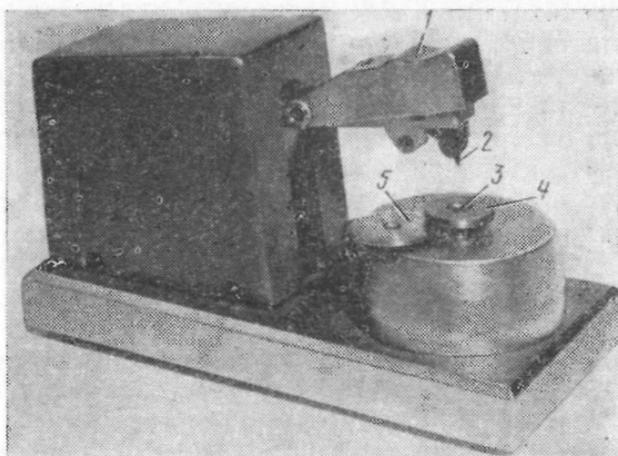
Приспособление для отрезки внутреннего витка спирали:
